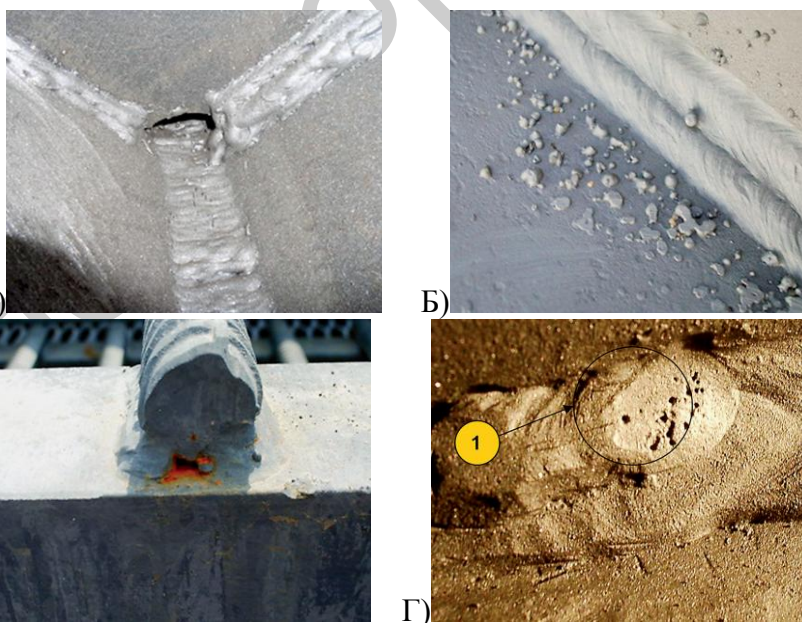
А – Неровный профиль сварного шва, 4Б – Сварочные брызги,
